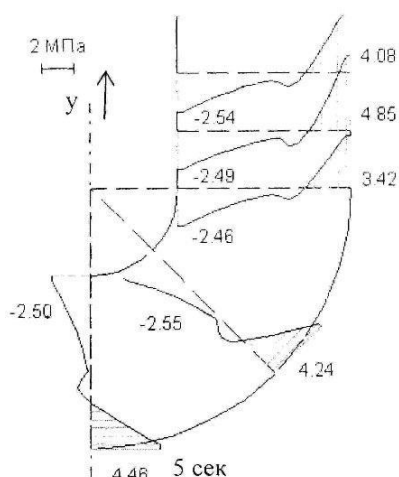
Эпюры напряжений σ_y в КОФ при затвердевании отливки
